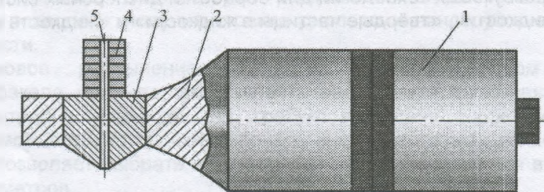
Схема передачи колебаний на сопло экструдера: 1 – преобразователь; 2 – излучатель; 3 – сопло; 4 – нагревательный элемент; 5 – канал подачи нити
